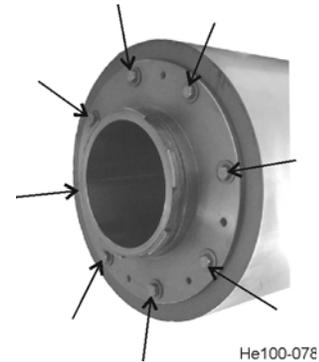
Desmontaje del tubo de los pernos de la camisa
